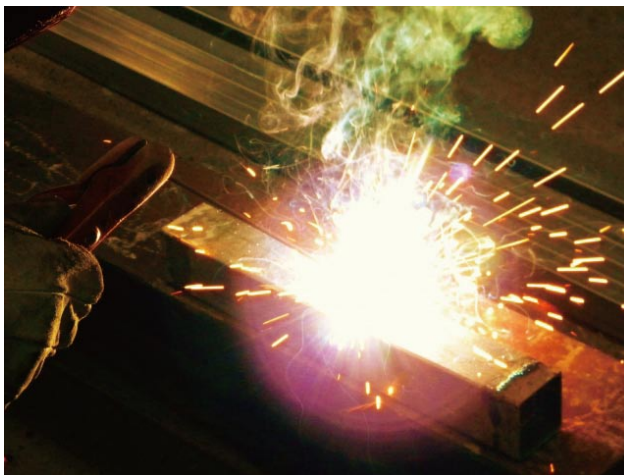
表層角膜炎は溶接作業でも起きる (photo AC 提供)
